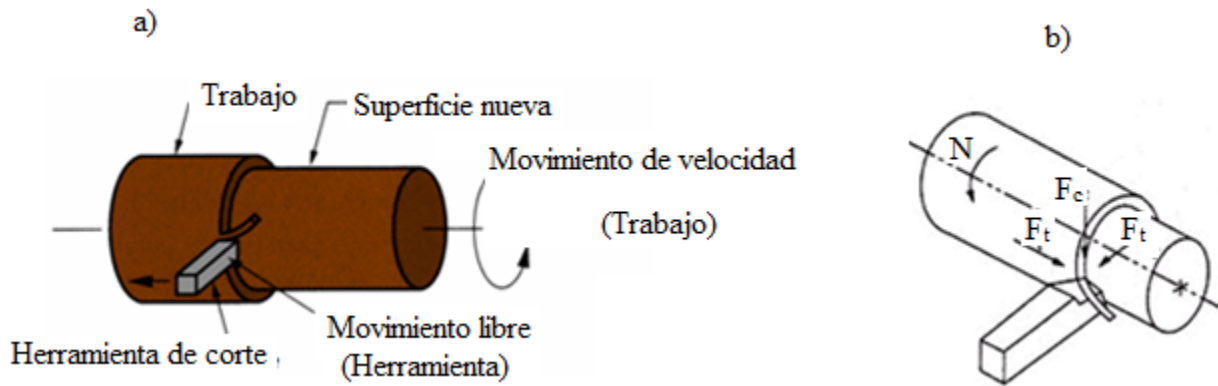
Torneado. a) Movimientos de corte, b) Fuerzas involucradas.
